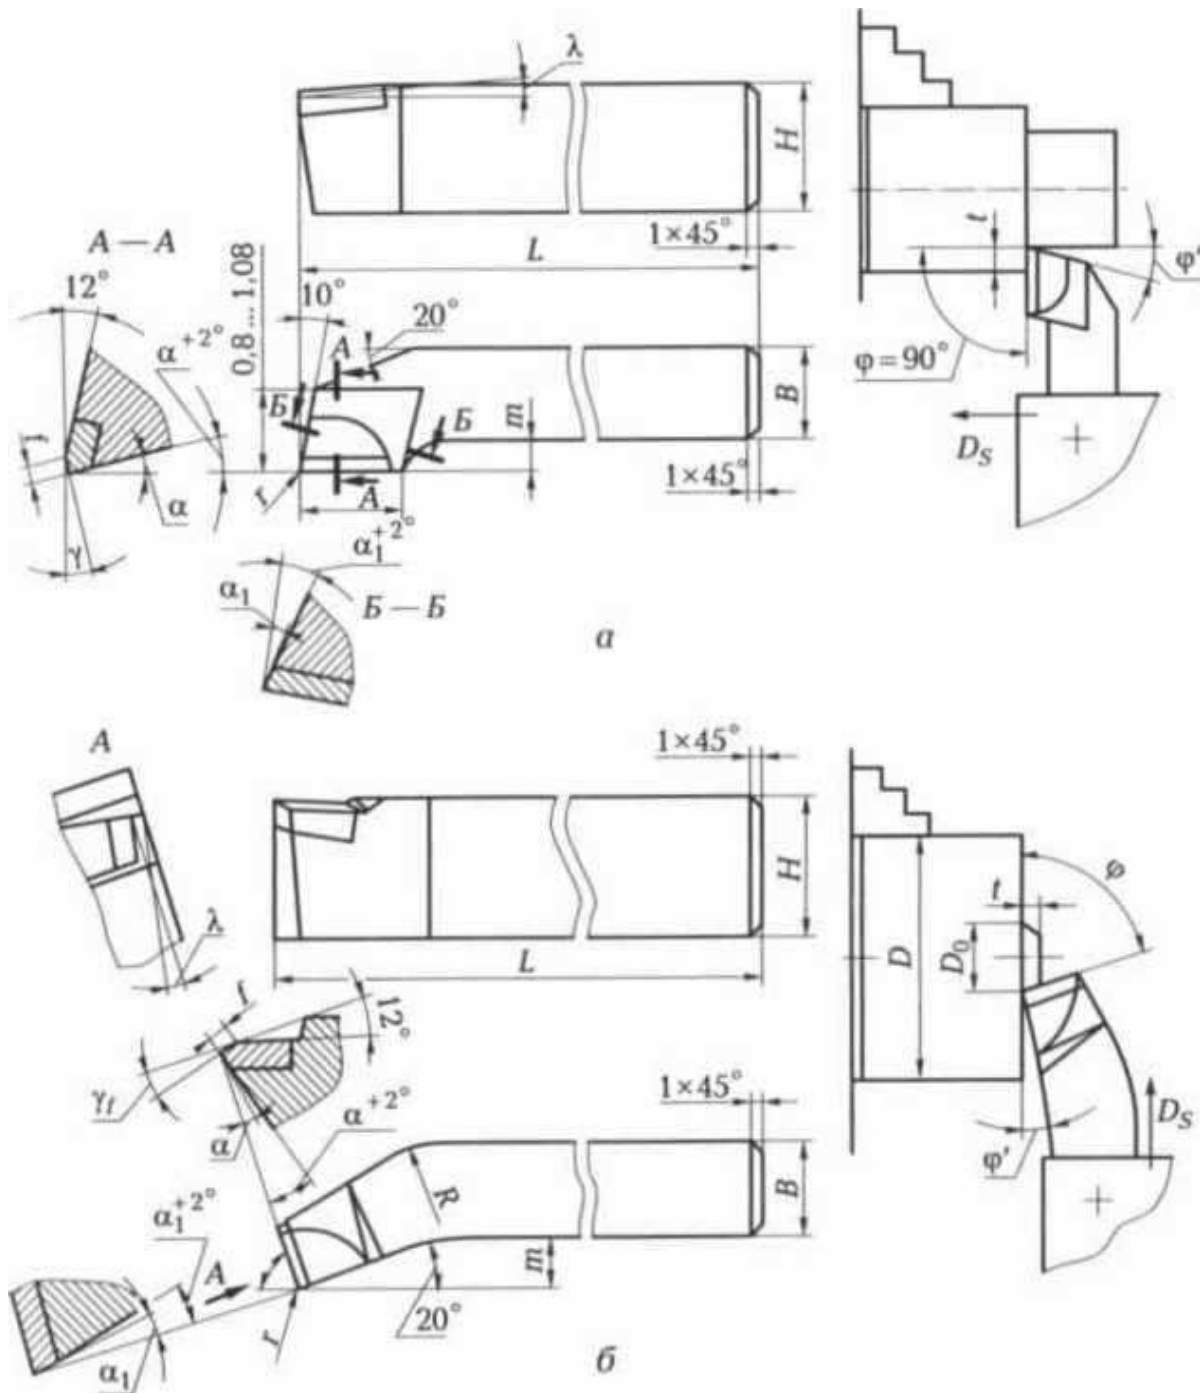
Токарные резцы, оснащенные пластинами из твердого сплава:
